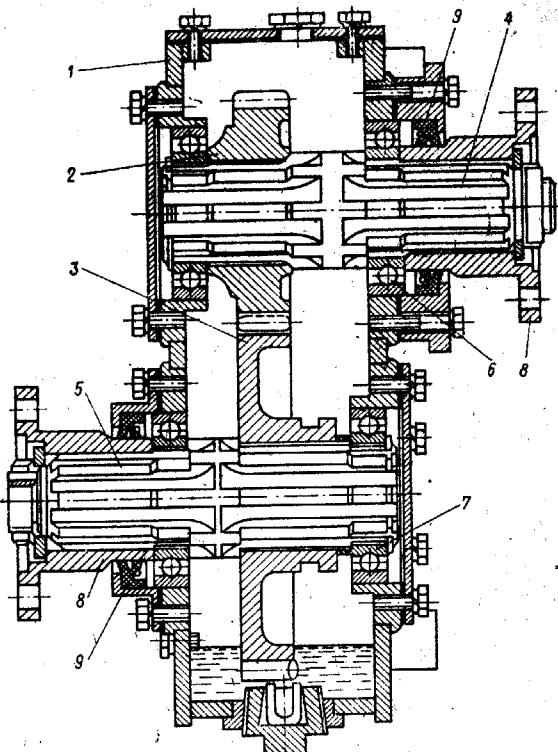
Синхронизирующий редуктор активного полуприцепа:
